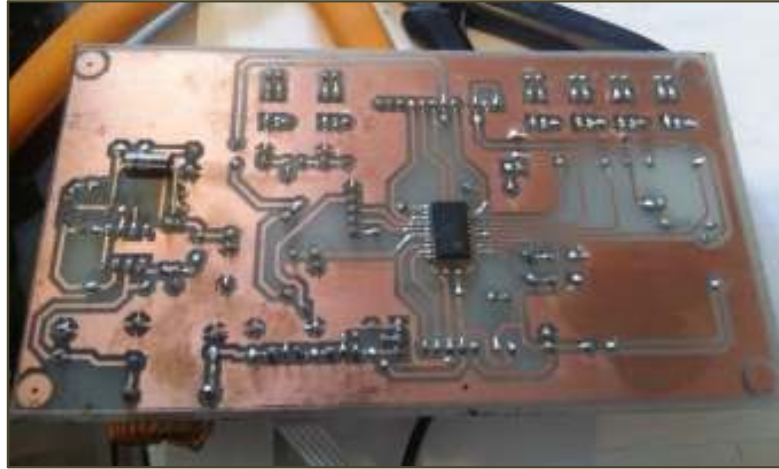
Montaje y soldadura del PICF18.
